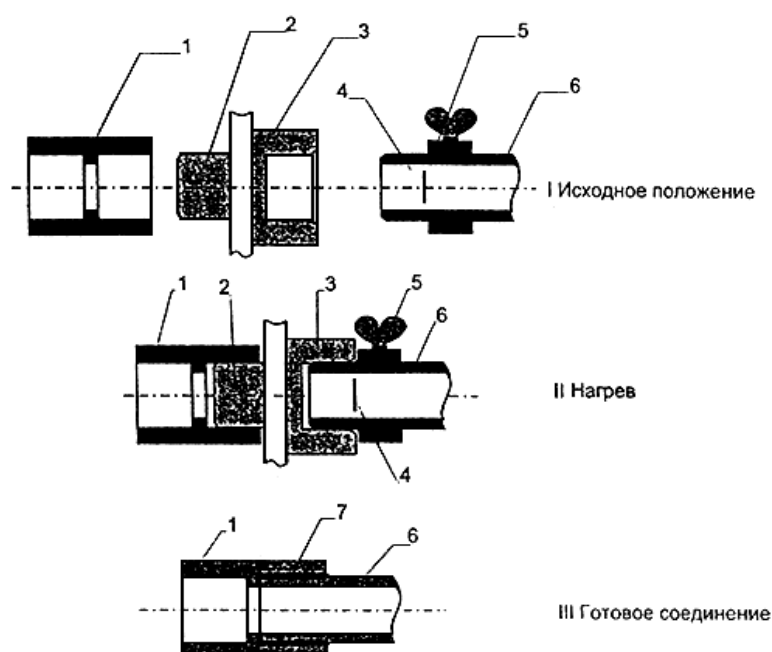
Последовательность процесса контактной сварки в раструб трубы и муфты из PPRC
